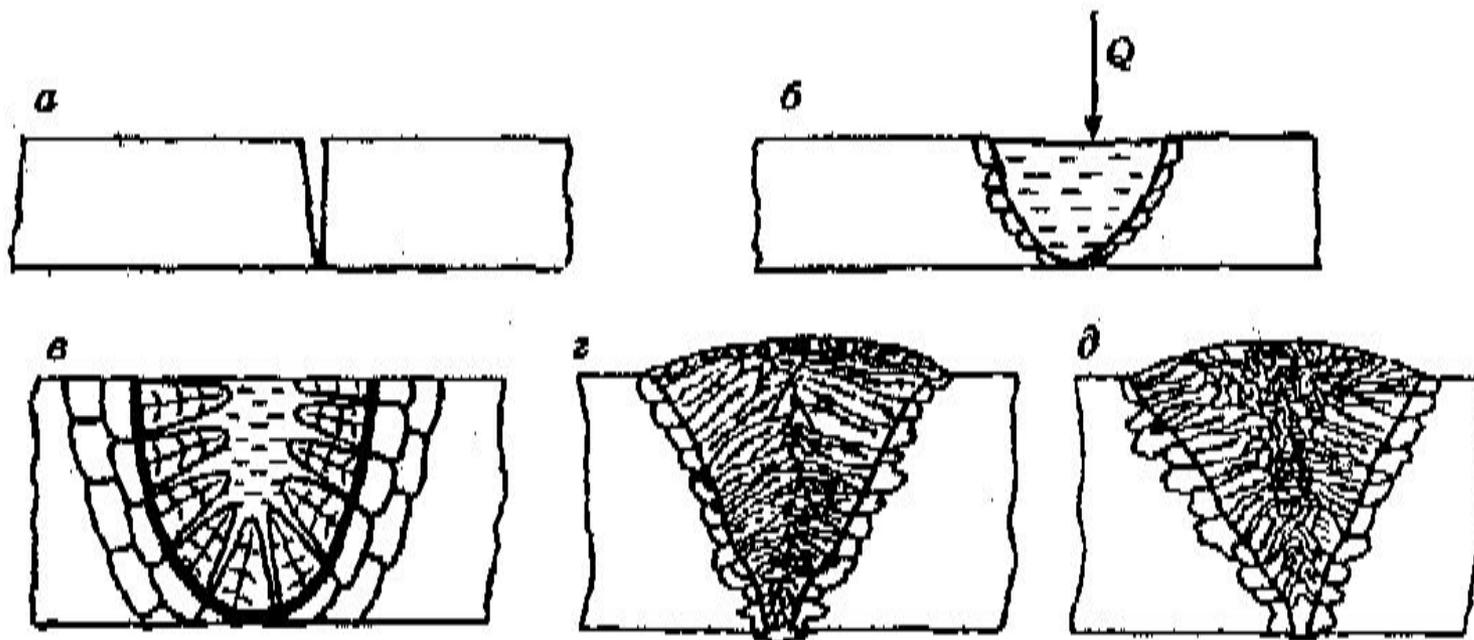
Схема образования сварного соединения при сварке плавлением:
